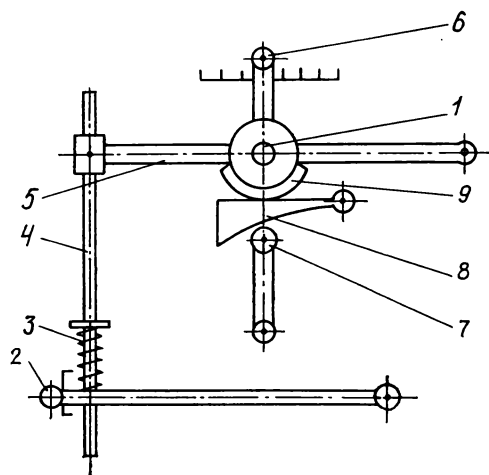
Схема тормозного устройства перематывателя 35П-5-М
